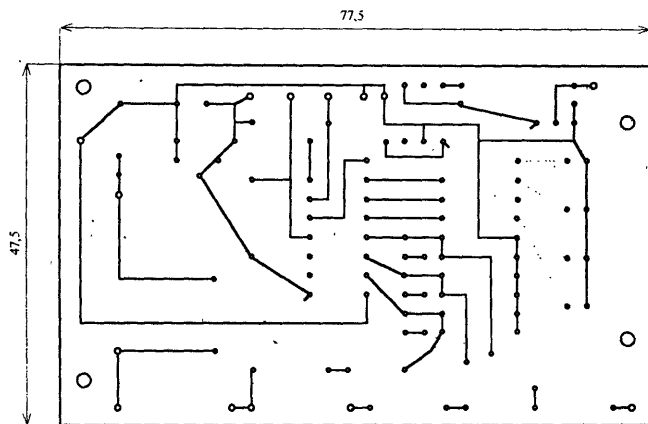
Устройство защиты трехфазных двигателей. Печатная плата
